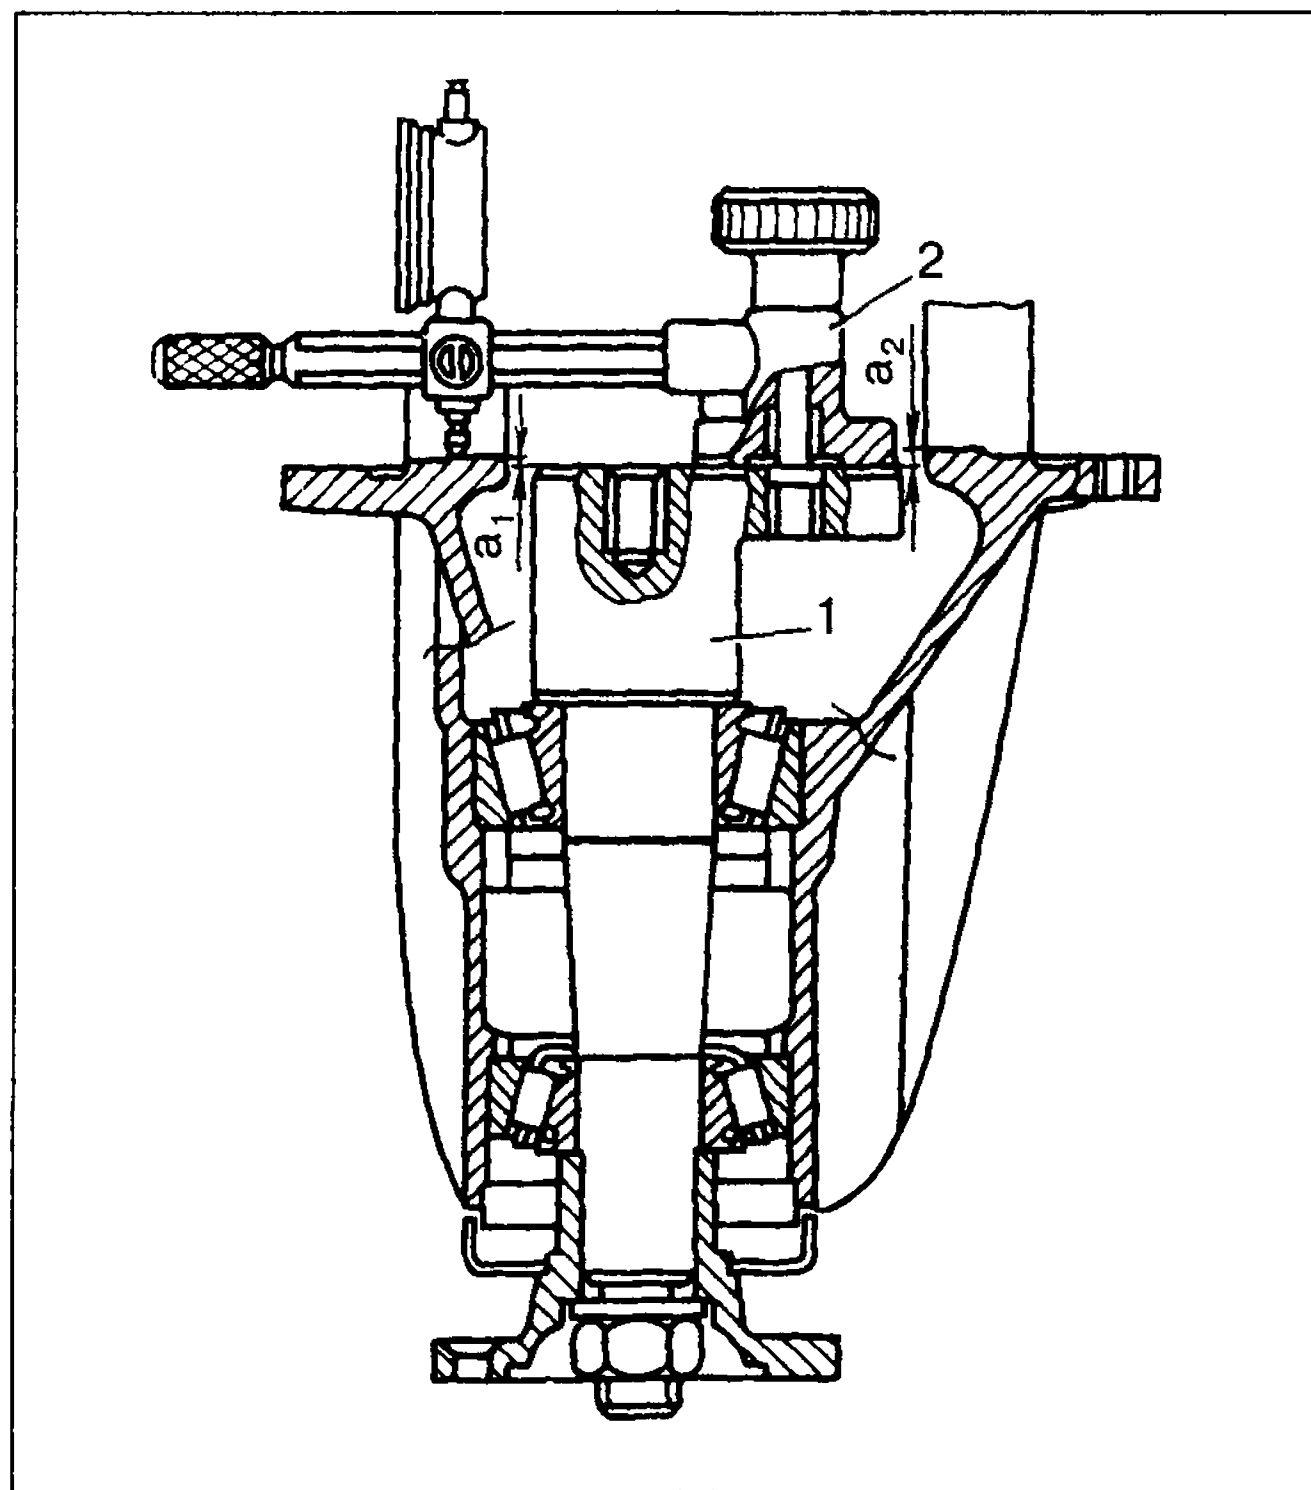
Схема снятия замеров для определения толщины регулировочного кольца ведущей шестерни:
